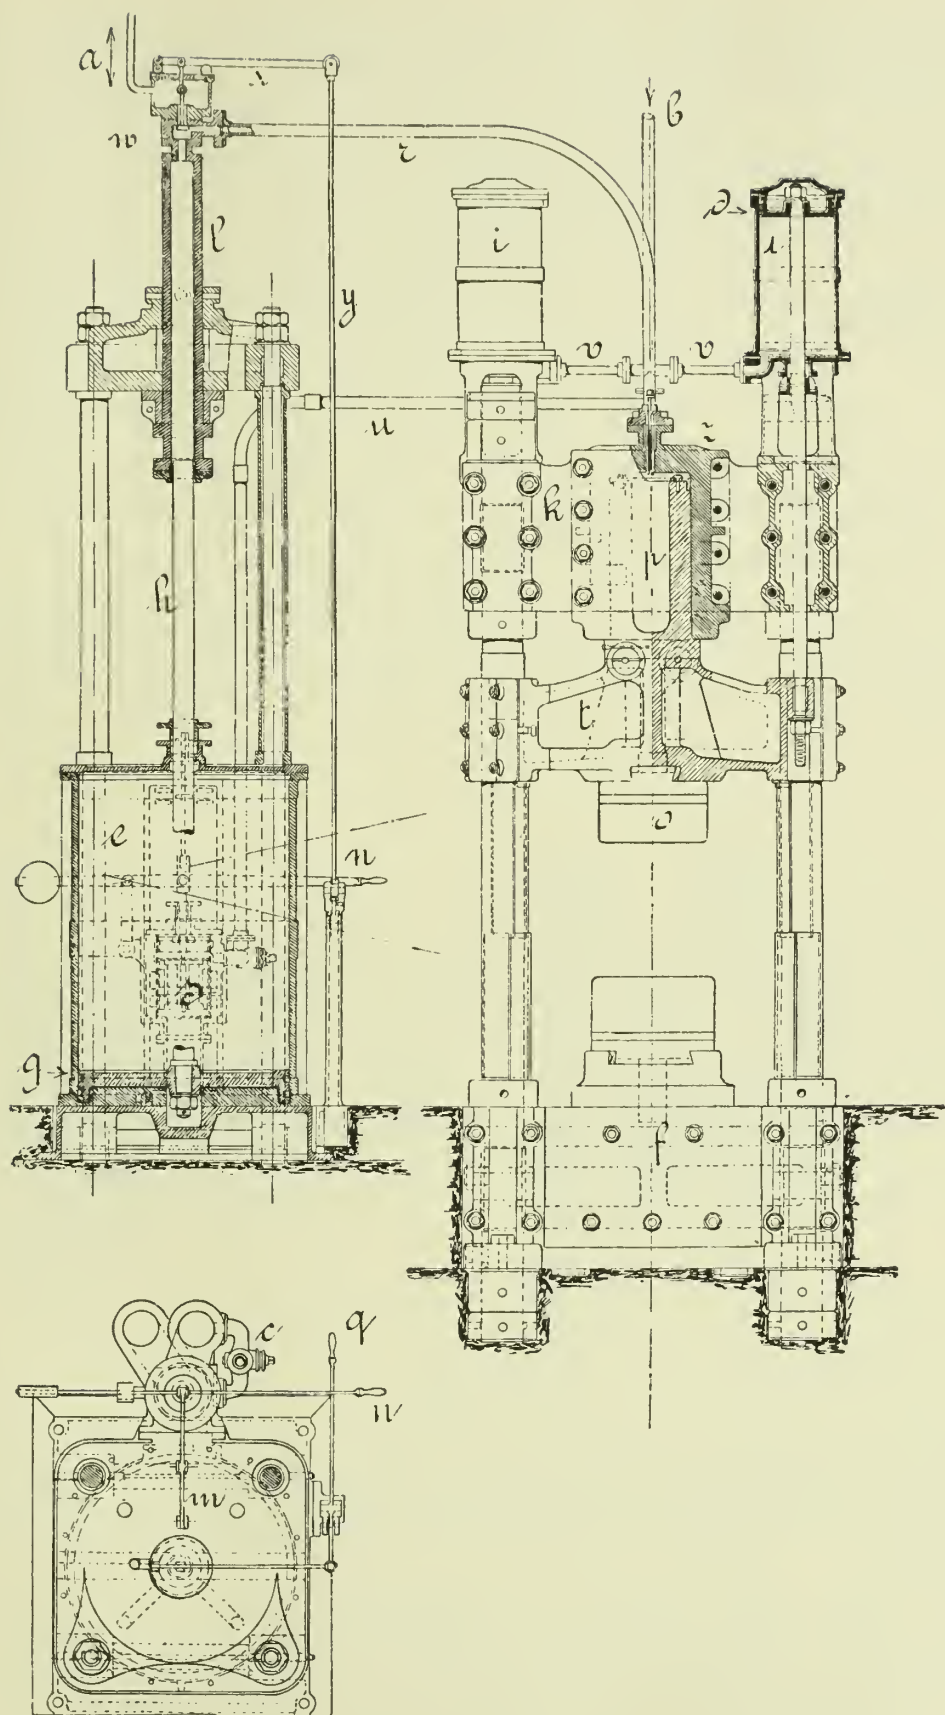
, 191. Hydraul. Schmiedepresse von Breuer, Schuhmacher & Ko.
